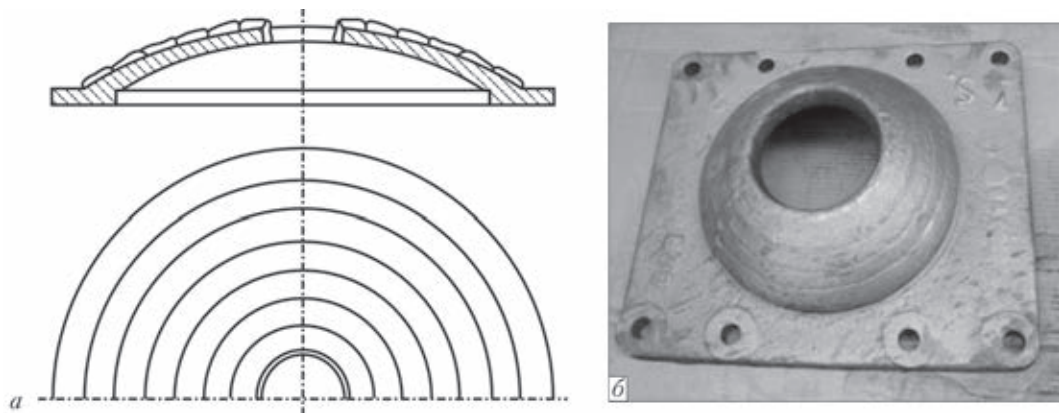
Схема литой цапфы поворота из стали 45Л (наружный диаметр 350 мм, толщина стенки 30 мм) (а) и внешний вид наплавленной детали (б) (толщина наплавленного слоя 4,0...13,8 мм)
